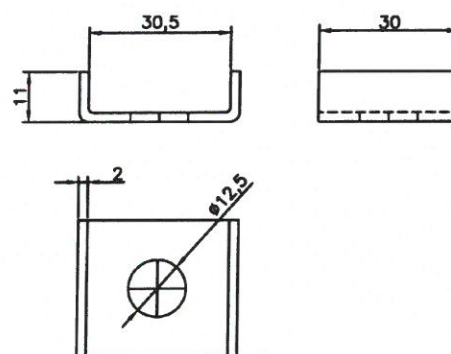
Wkładki stalowe punktów stałych QuickStream do uchwytów i obejm
